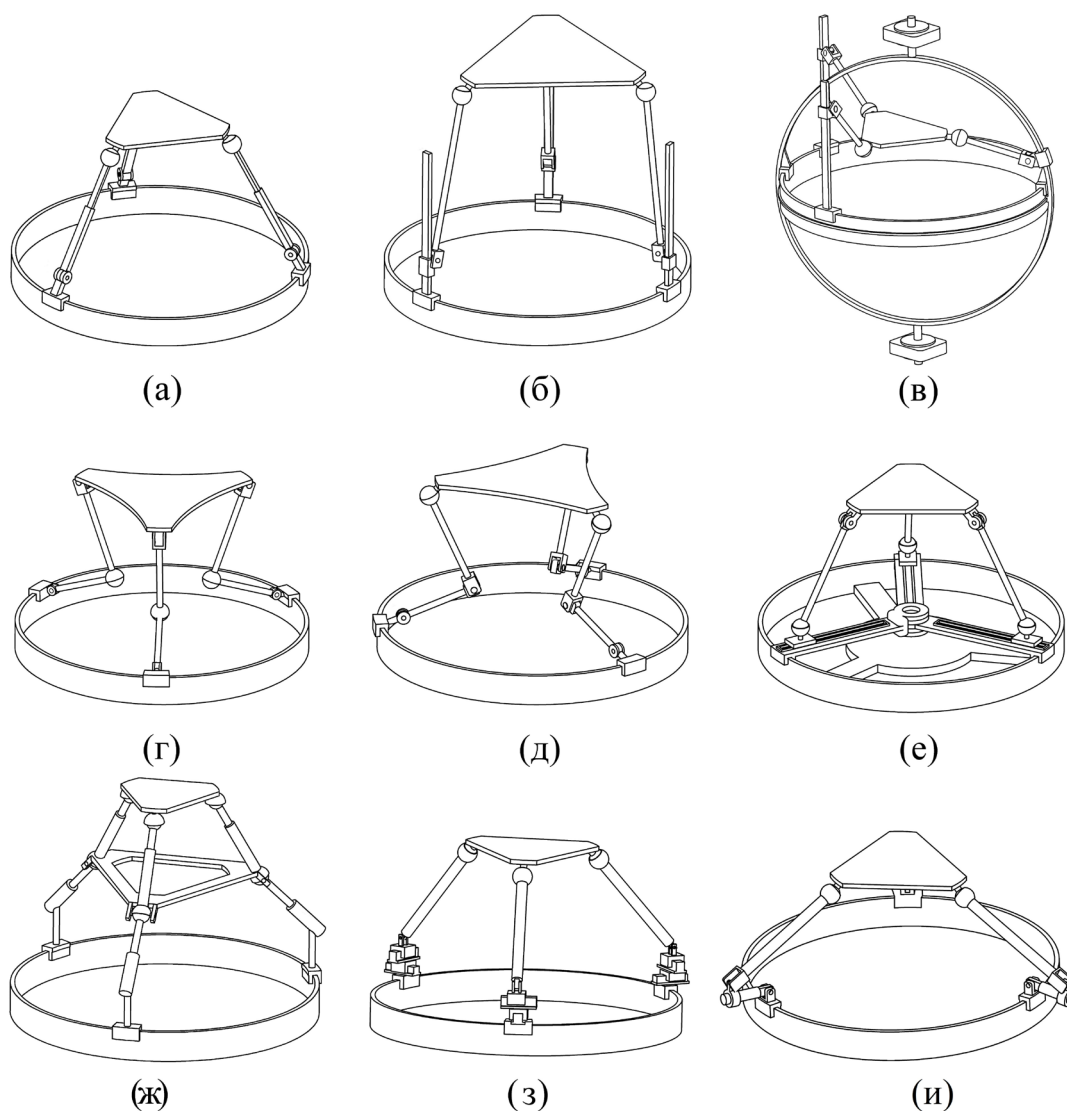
Шести- и девятиподвижные механизмы параллельной структуры с круговой направляющей и тремя кинематическими цепями
